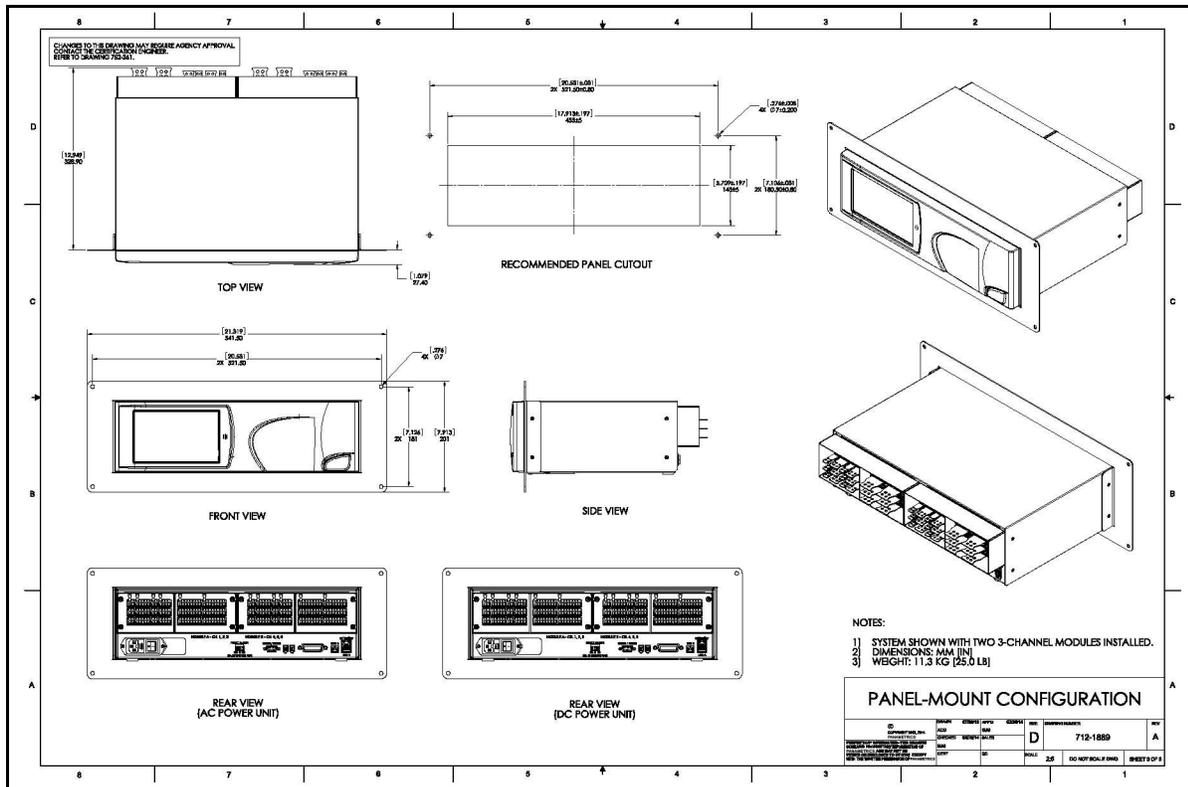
Version für Tafelmontage (Zeichnung 712-1889_revA, Blatt 3 von 3)
